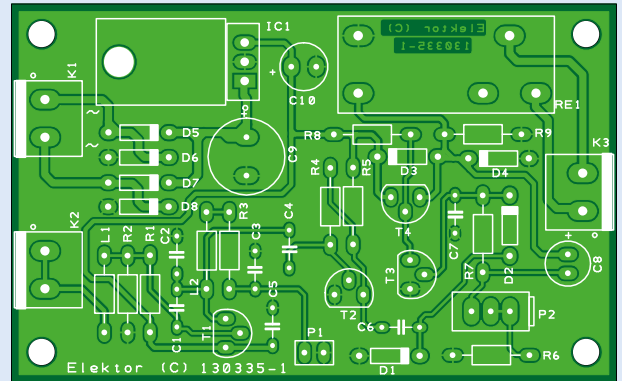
Auf der Platine ist die Schaltung schnell montiert, sie besteht ausschließlich aus bedrahteten Bauelementen.
